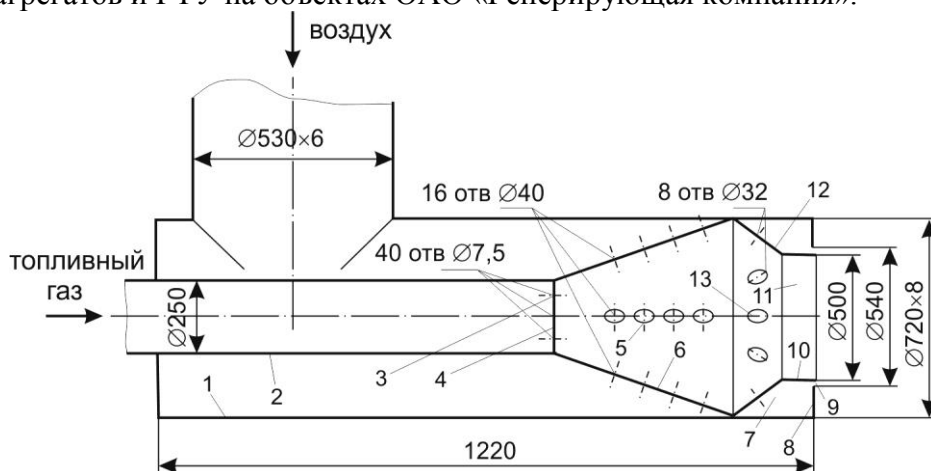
Схема горелочного устройства: 1, 2 – воздушный и газовый тракты; 3 – отверстия в шайбе 4 для распределения газового потока; 5 – отверстия для прохода воздушного потока в диффузор 6; 7 – камера для снижения скорости газозвушной смеси; 8 – шайба; 9 – кольцевая щель; 10 – цилиндрическая часть смесителя; 11 – огневое отверстие; 12 – конфузор смесителя с отверстиями 13.
